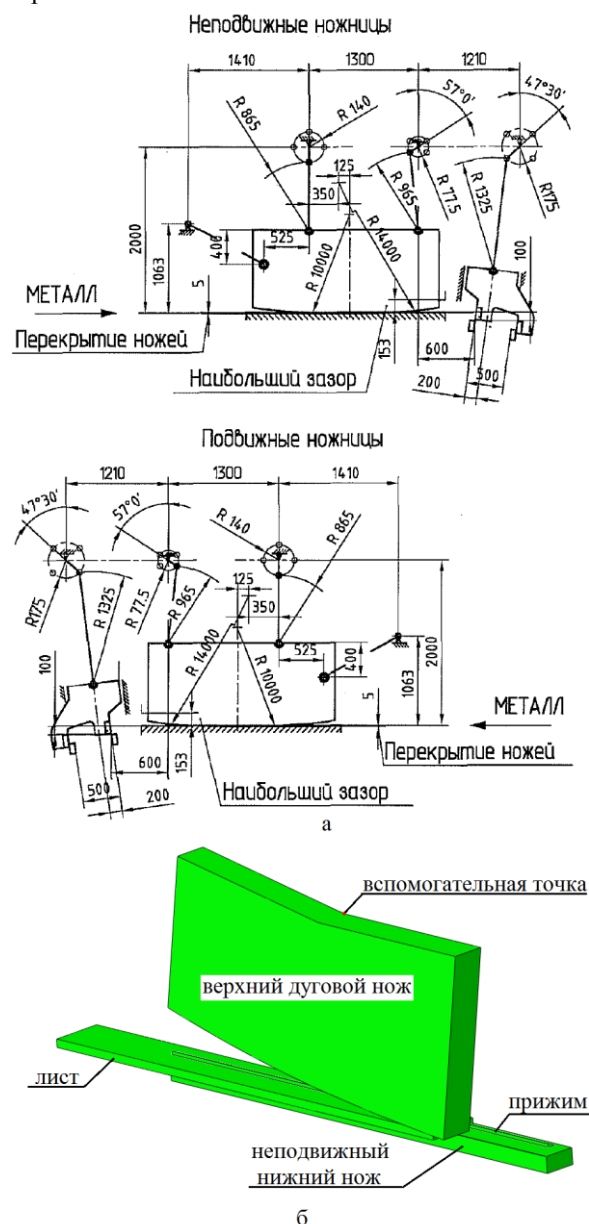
СКОН стана 2800 ПАО «Ашинский металлургический завод» (Россия) конструкции НКМЗ: а – кинематическая схема механизмов резания, б – общий вид модели процесса обрезки кромок дуговым ножом на ножницах с катящимся резом
